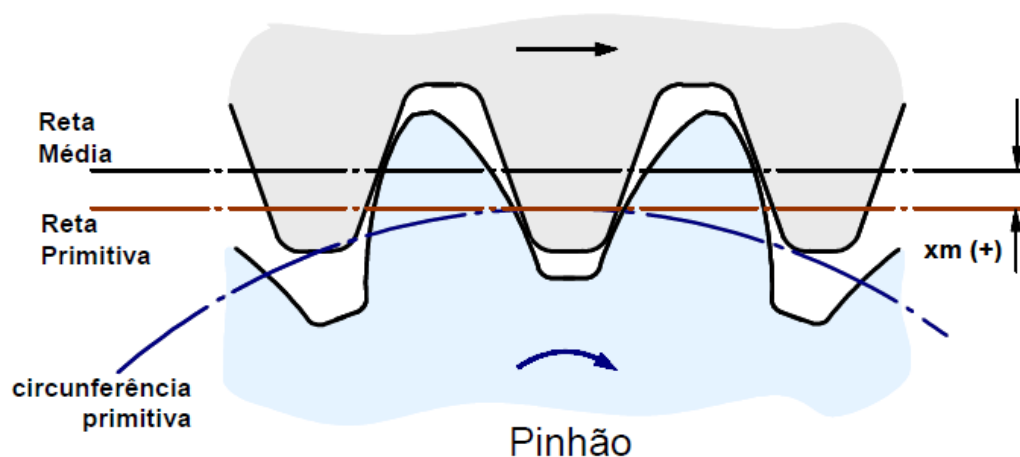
Efeito do deslocamento de perfil na fabricação de uma engrenagem. (retirada de Gemaque, 2004)
